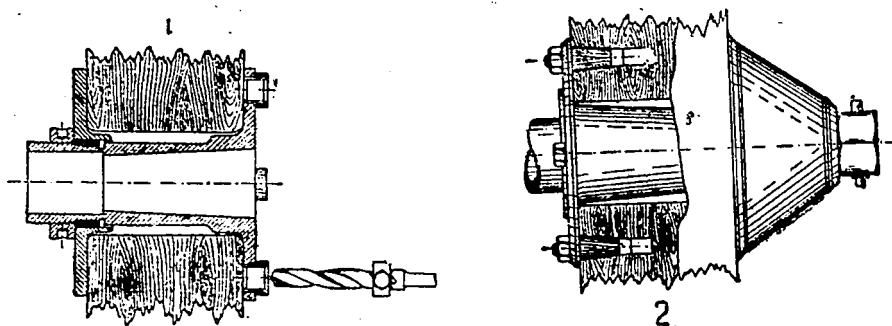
1. Сверловка болтовых отверстий с помощью кондуктора Руппа. 2. Втулка Руппа с правильно установленным винтом.
